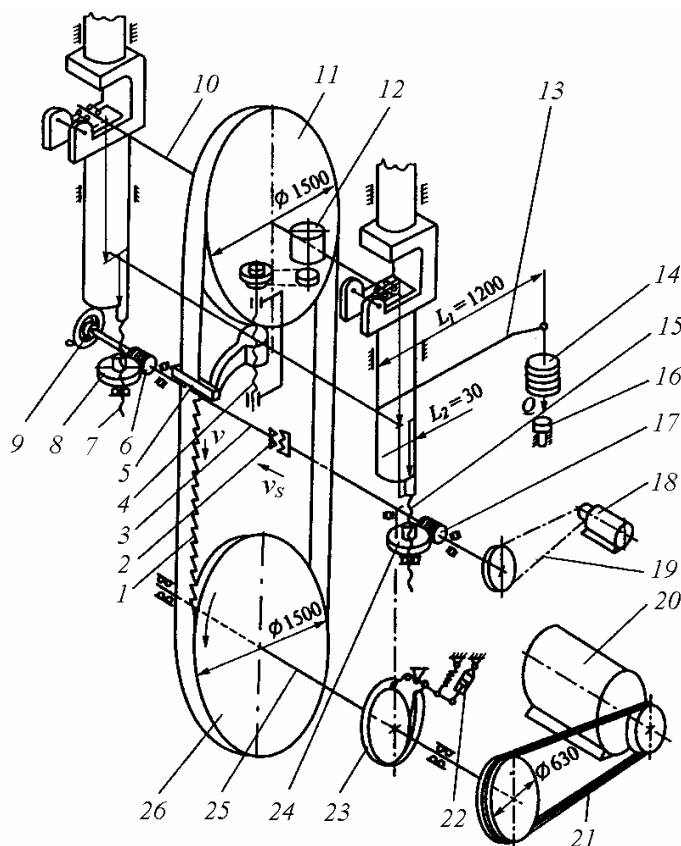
Кинематическая схема механизма резания вертикального ленточнопильного станка (ЛБ150-1)
